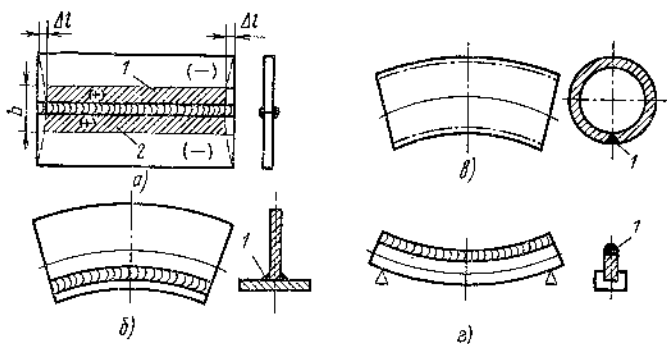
Деформации сварных изделий от продольной усадки наплавленного металла:
